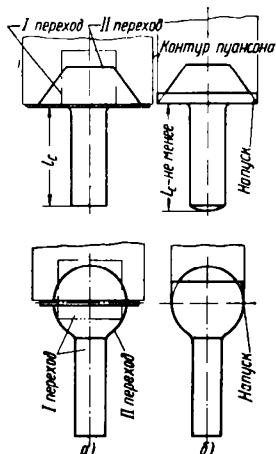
Варианты штамповки поковки с конической и шаровидной головками: а — в открытом; б — в закрытом штампе
